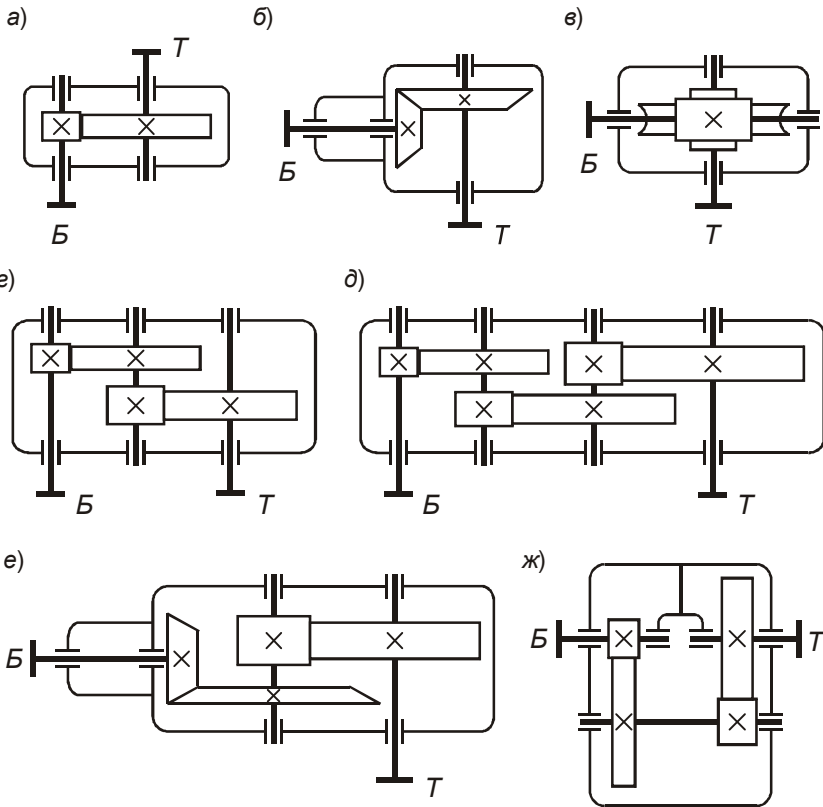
Схемы редукторов: *а* – цилиндрический одноступенчатый; *б* – конический одноступенчатый; *в* – червячный одноступенчатый; *г* – цилиндрический двухступенчатый развернутой схемы; *д* – цилиндрический трехступенчатый развернутой схемы; *е* – коническо-цилиндрический двухступенчатый; *ж* – соосный двухступенчатый
